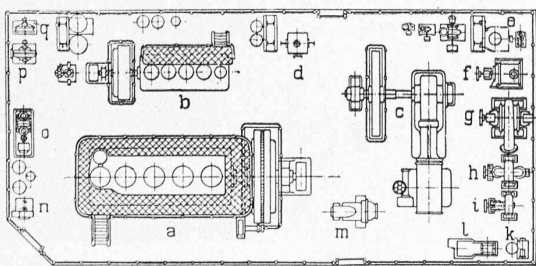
Ausstellung von Gebr. Sulzer, A.-G. — Grundriss 1 : 300.
